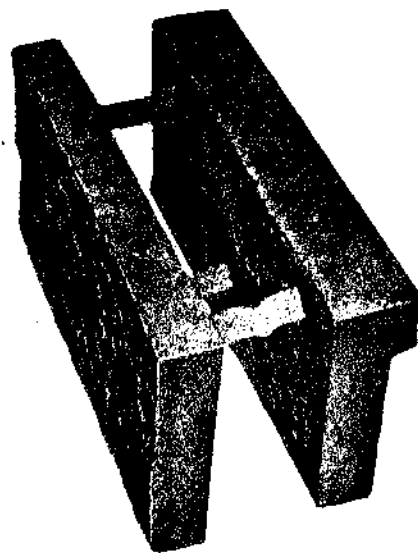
Pieza soldada en un horno rotatorio.
